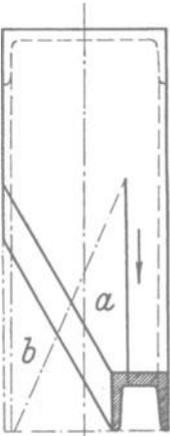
Profilverjüngung durch Schweißen.
